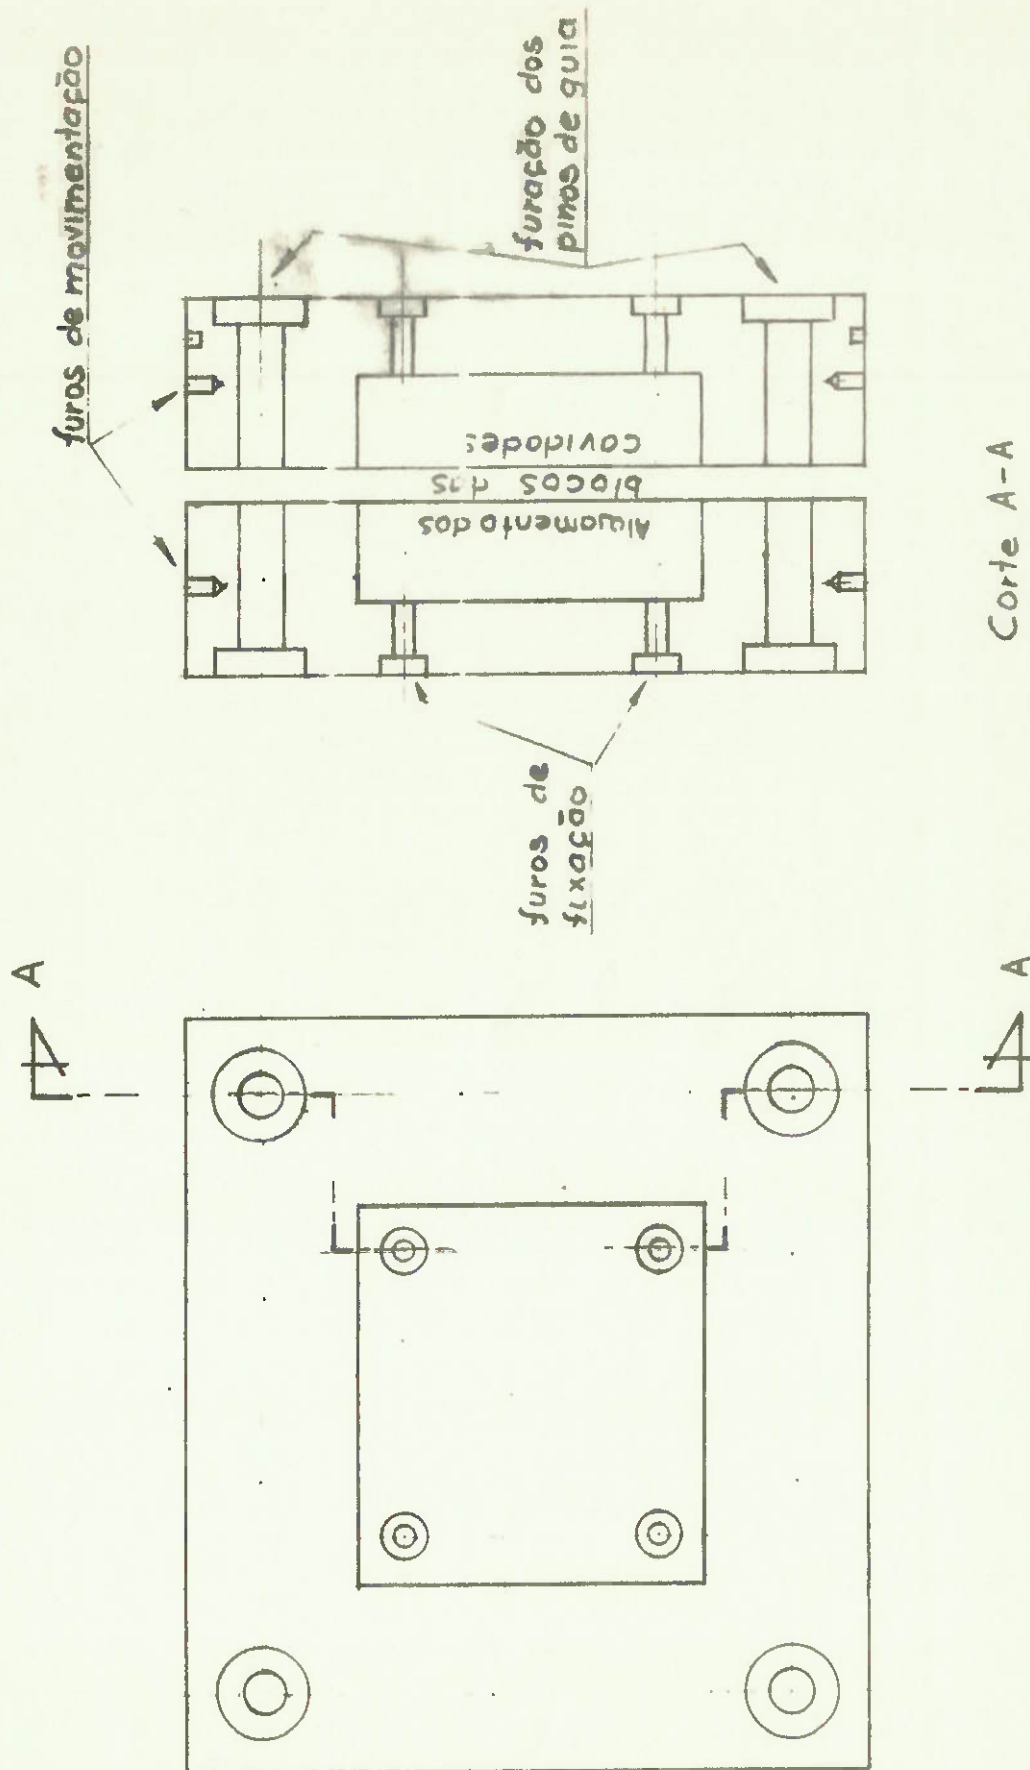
Vista da caixa do molde mostrando as cavidades dos machos, e a furação dos pinos e buchas de guia e extratores.
